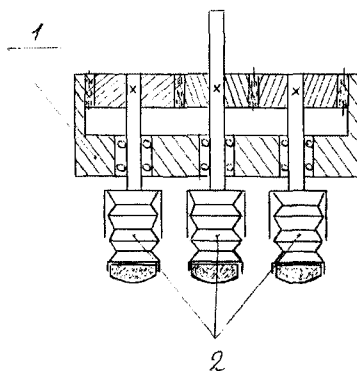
Инструмент - платформа, обеспечивающая вращение сильфонов, несущих обрабатывающие головки, каждого в отдельности: 1 - платформа с приводной шестерней; 2 - сильфоны, установленные в платформу с помощью подшипников, и имеющие, на одном конце шестерню для привода, а на другом конце обрабатывающие головки.
